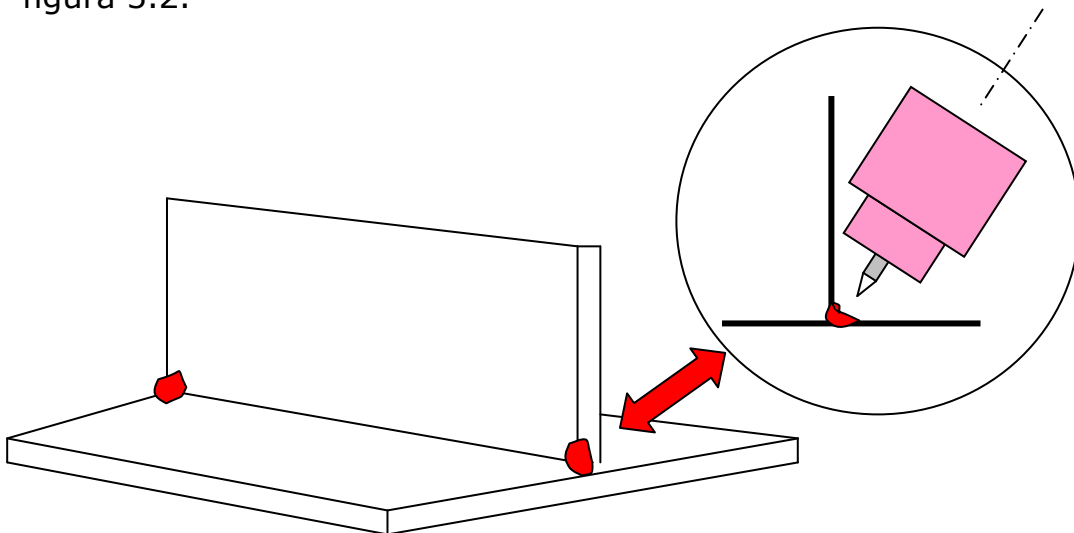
Punteado para obtener el ensamblaje de soldadura de filete entre placas.
